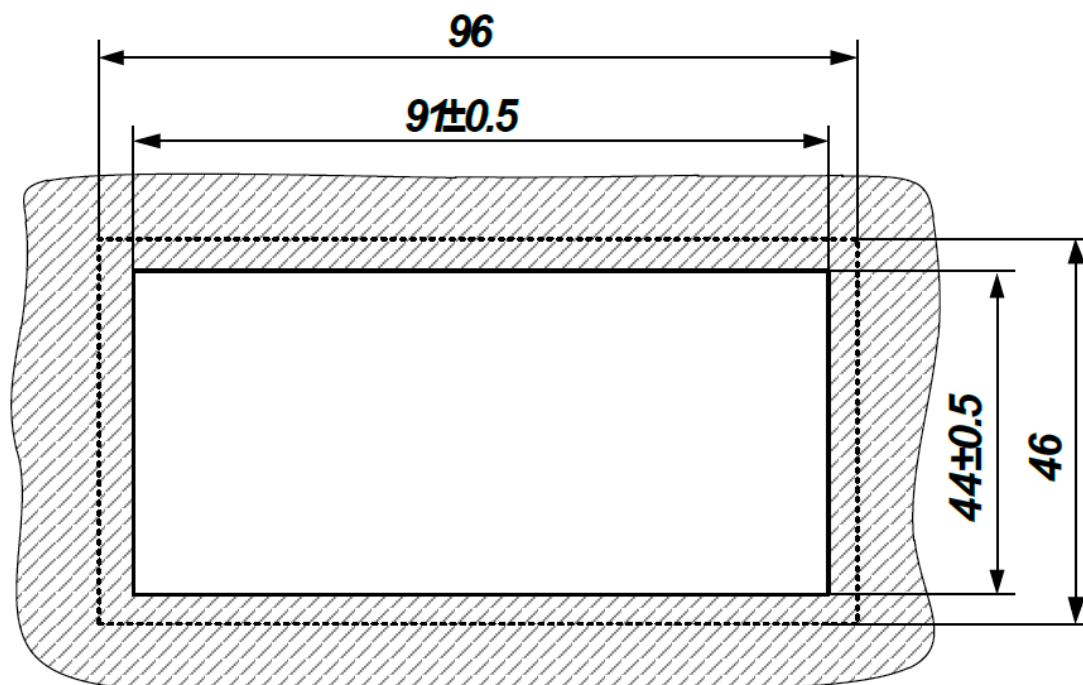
Размеры вырубного отверстия в щите для установки Прибора
